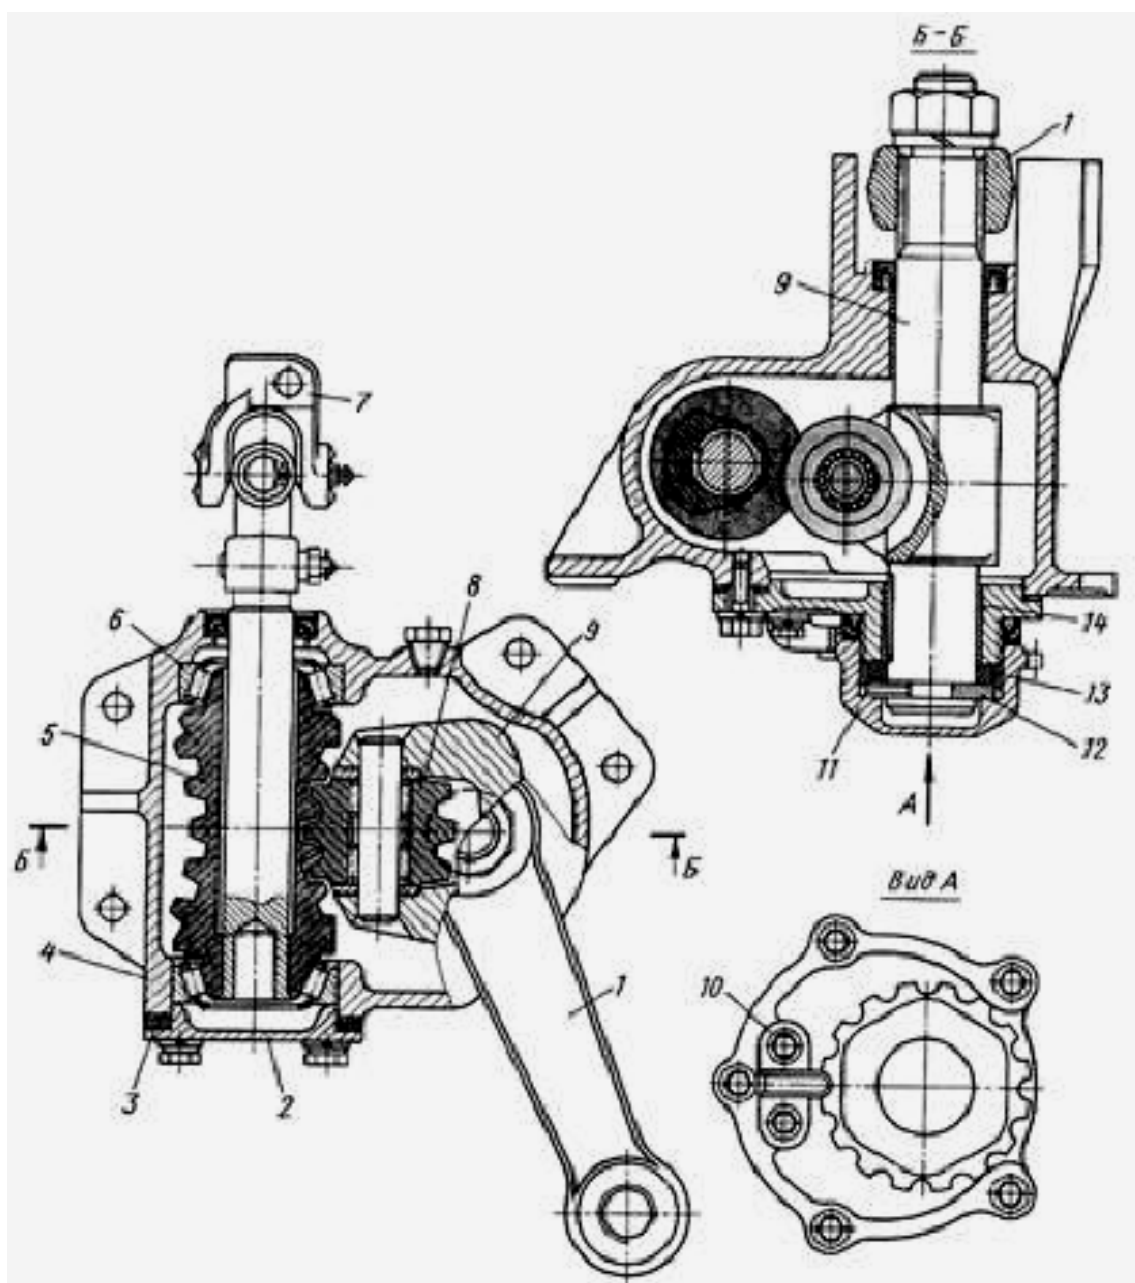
Рулевой механизм автомобиля КАЗ-608 «Колхида»: 1 - рулевая сошка; 2 - крышка; 3 - регулировочные прокладки; 4 - картер; 5 - глобоидный червяк; 6 - конический роликовый подшипник; 7 - карданный шарнир; 8 - трехгребневый ролик; 9 - вал сошки; 10 - стопор; 11 - гайка; 12 - упорная шайба; 13 - регулировочные прокладки; 14 - крышка
